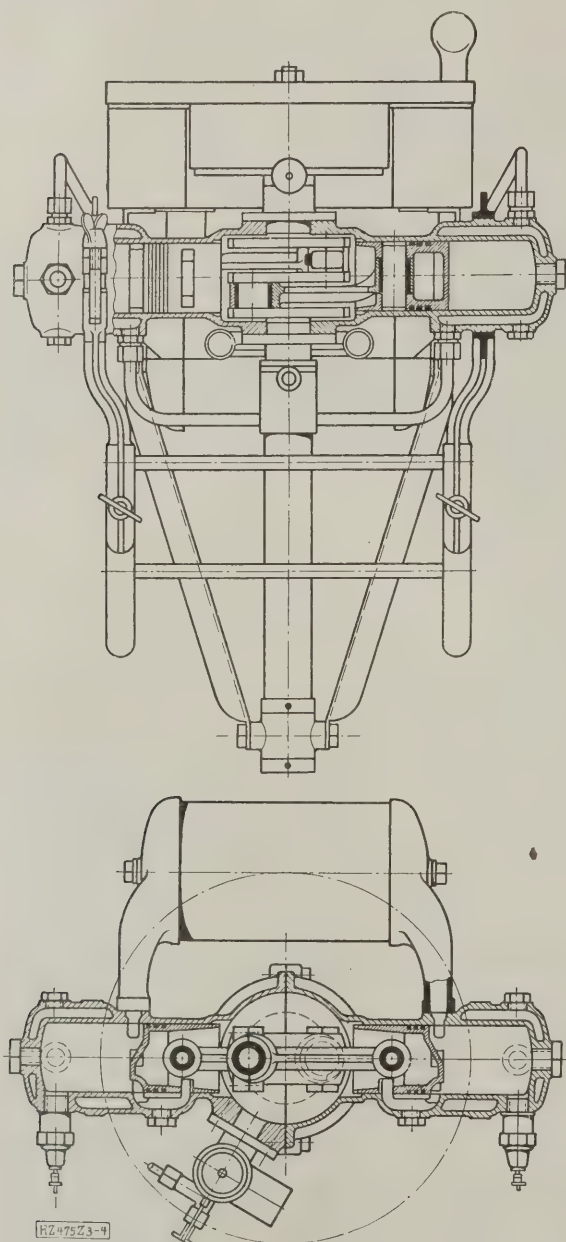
und 4. Senkrechter und wagerechter Schnitt durch die Zylinder.
